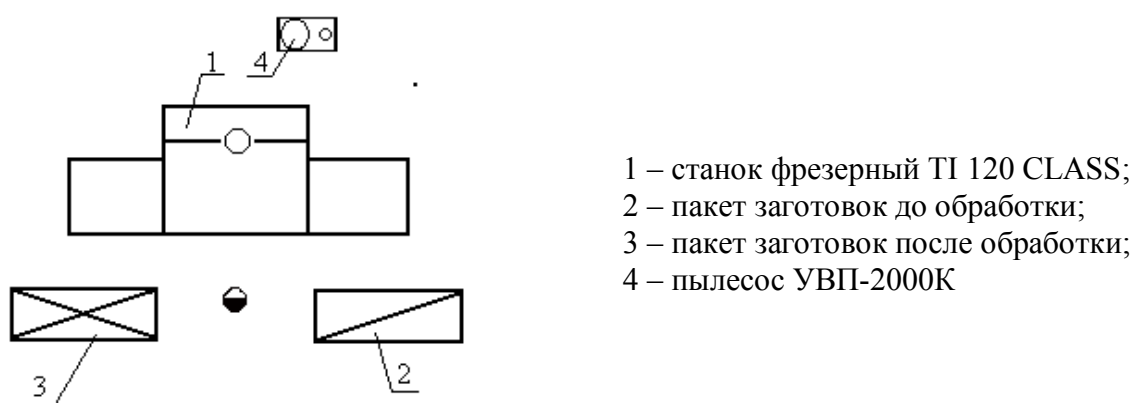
План рабочего места у фрезерного станка TI 120 CLASS
